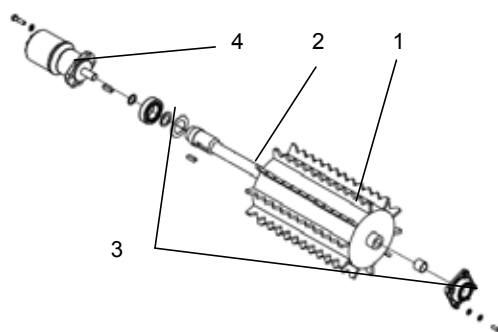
Верхний обжимной горизонтальный валец на вращающемся валу в сборе с гидромотором подающего устройства рубильной установки Junkkari HJ500C: 1 – валец; 2 – вал; 3 – подшипник и подшипниковая опора; 4 – гидромотор
